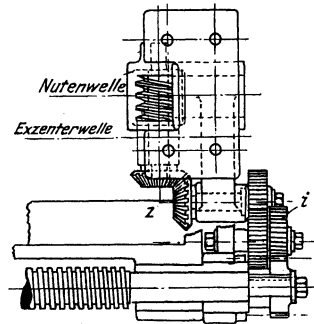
Der Antrieb für die Spiralen-Erzeugung.
